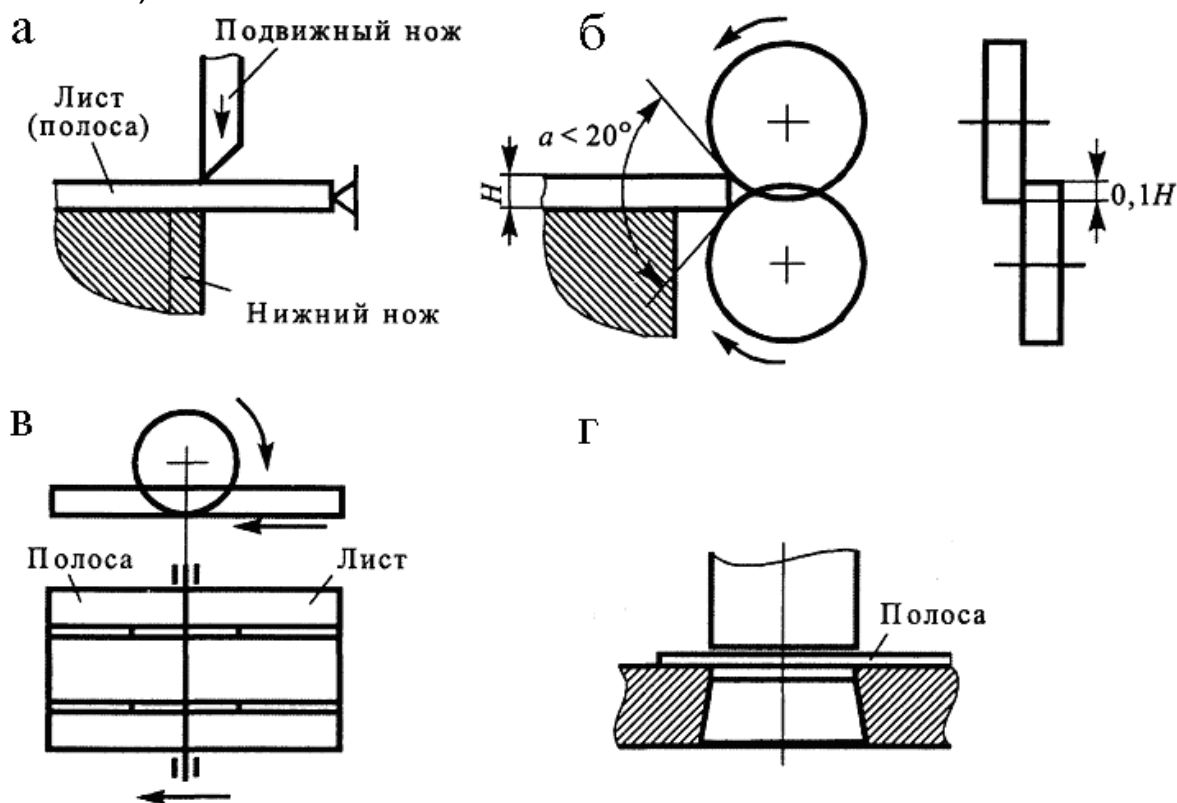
15. Получение заготовок: резанием на гильотинных (а) и роликовых (б) ножницах, дисковыми фрезами (в) и штамповкой (г)
